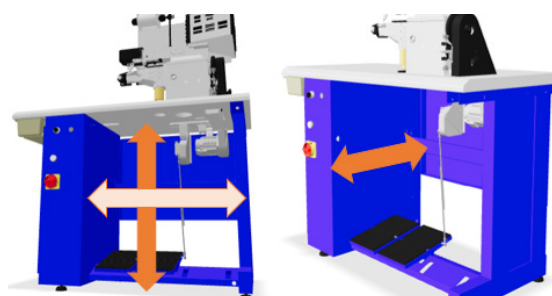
Dimensiones recomendadas para el espacio libre para las piernas en el puesto de doblado.
